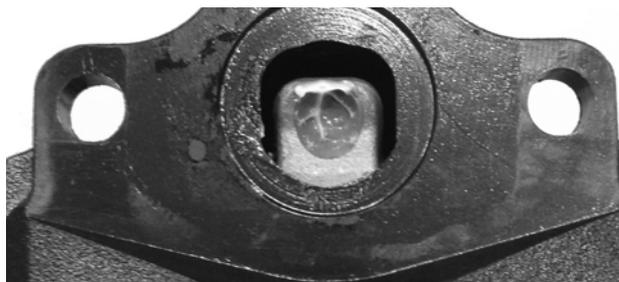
Superficies de montaje de la cámara de frenos del caliper
